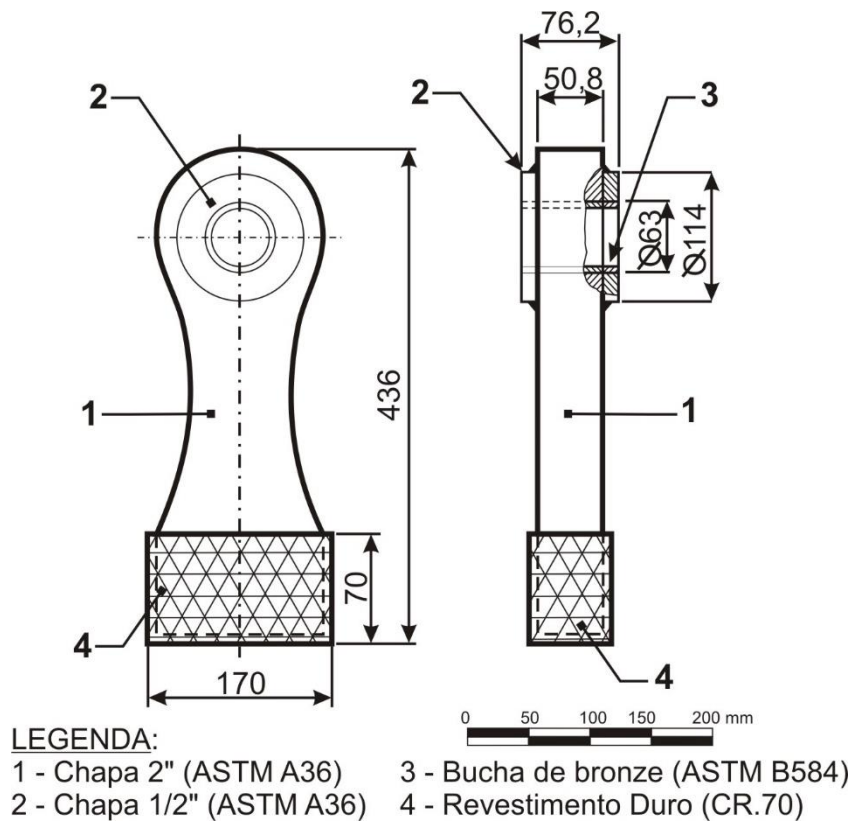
Desenho técnico do martelo e seus componentes [28].
